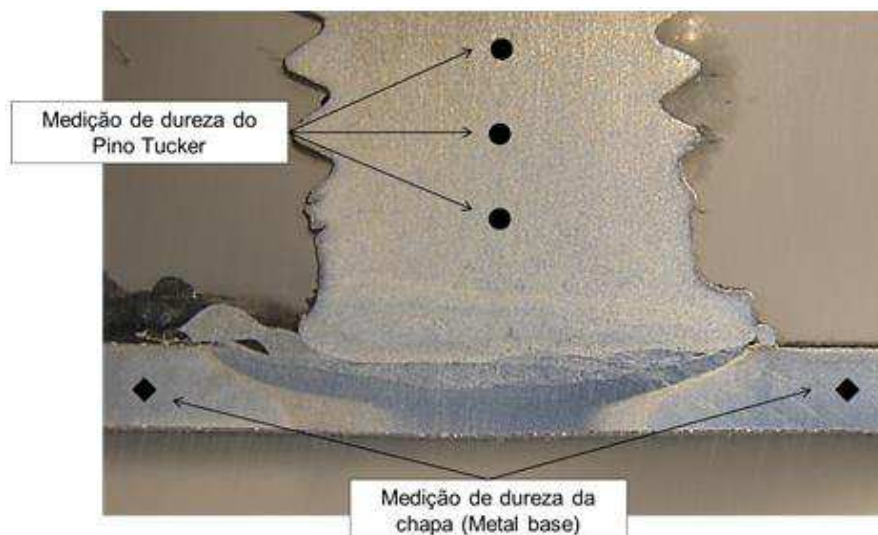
Esquema da medição de dureza do Pino Tucker e da Chapa Hot Stamping.
